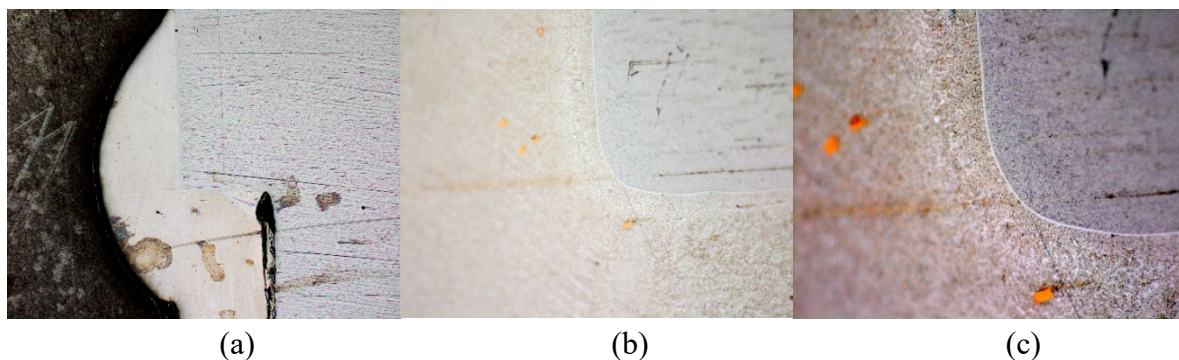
Шлиф стыкового сварнопаяного соединения: (a)- общий вид соединения; (b)- сварнопаяный шов; (c)- интерметаллидная прослойка толщиной 1-2 мкм
